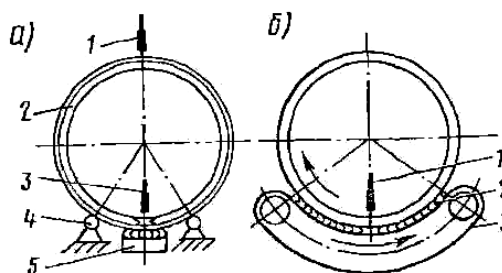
Схемы стендов для автоматической сварки котла цистерны при наложении стыковых продольных (а) и кольцевых (б) швов
